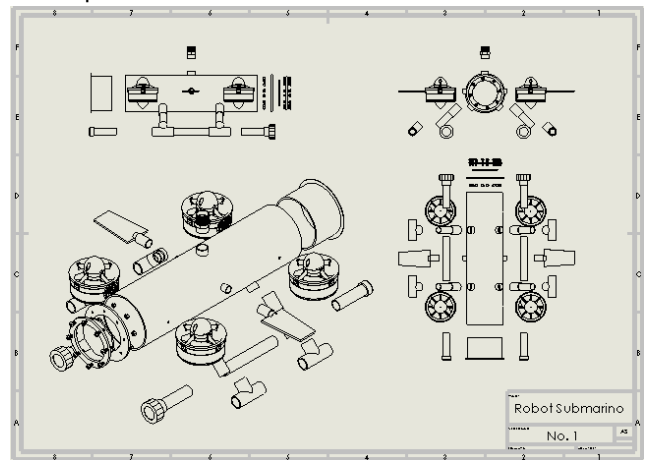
Vista explosionada del ROV [Fuente: Elaboración propia].
